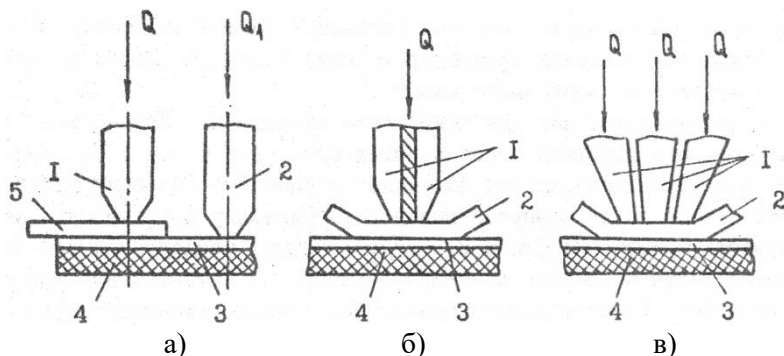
Схемы односторонней контактной сварки: а – односторонняя точечная сварка: 1 – электрод для сжатия свариваемых деталей и подвода тока к проволоке; 2 – электрод для подвода тока к шине печатной платы; 3 – контактная площадка или шина печатной платы; 4 – диэлектрическое основание печатной платы; 5 – привариваемая проволока или лента; б и в – односторонняя сварка соответственно сдвоенным электродом (с параллельными зазорами) и строенным электродом трехфазным (1 – электроды; 2 – привариваемый проводник; 3 – тонкая металлическая пленка; 4 – диэлектрическая подложка)
